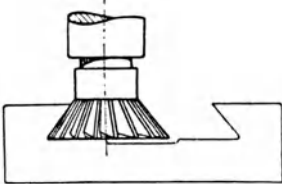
Fräsen mit dem Winkelstirnfräser.
